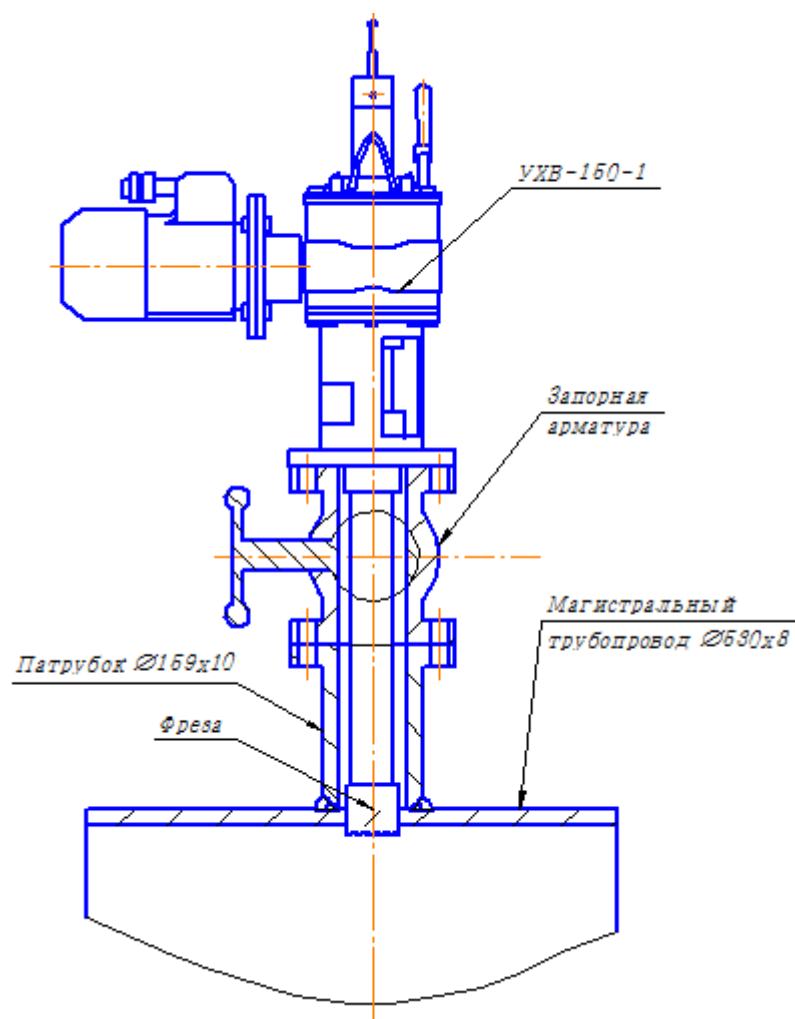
Установка типа УХВ-150- 1 для фрезерования отверстия
